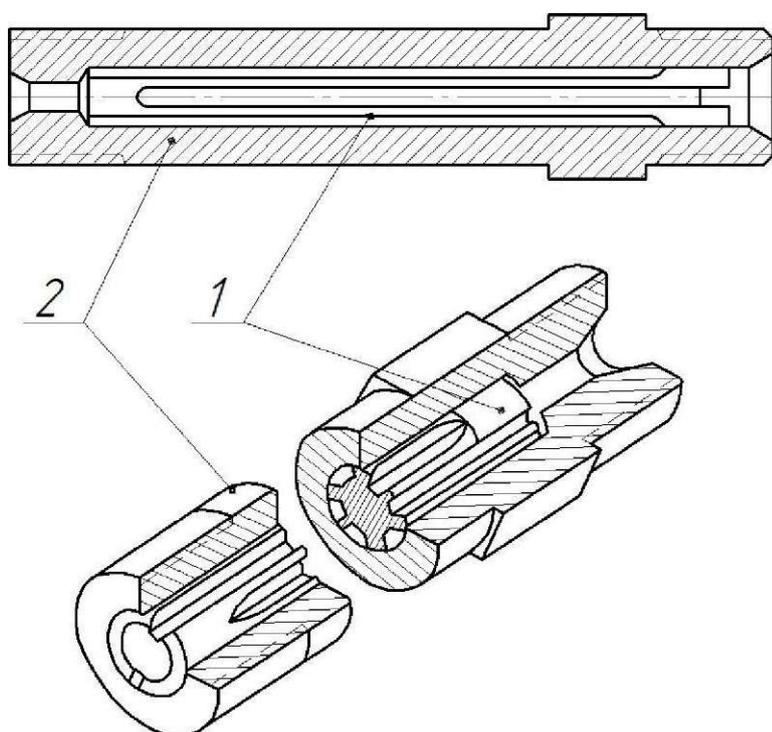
Щелевой фильтр высокого давления 1 - Фильтрующий элемент; 2 - Корпус фильтра
